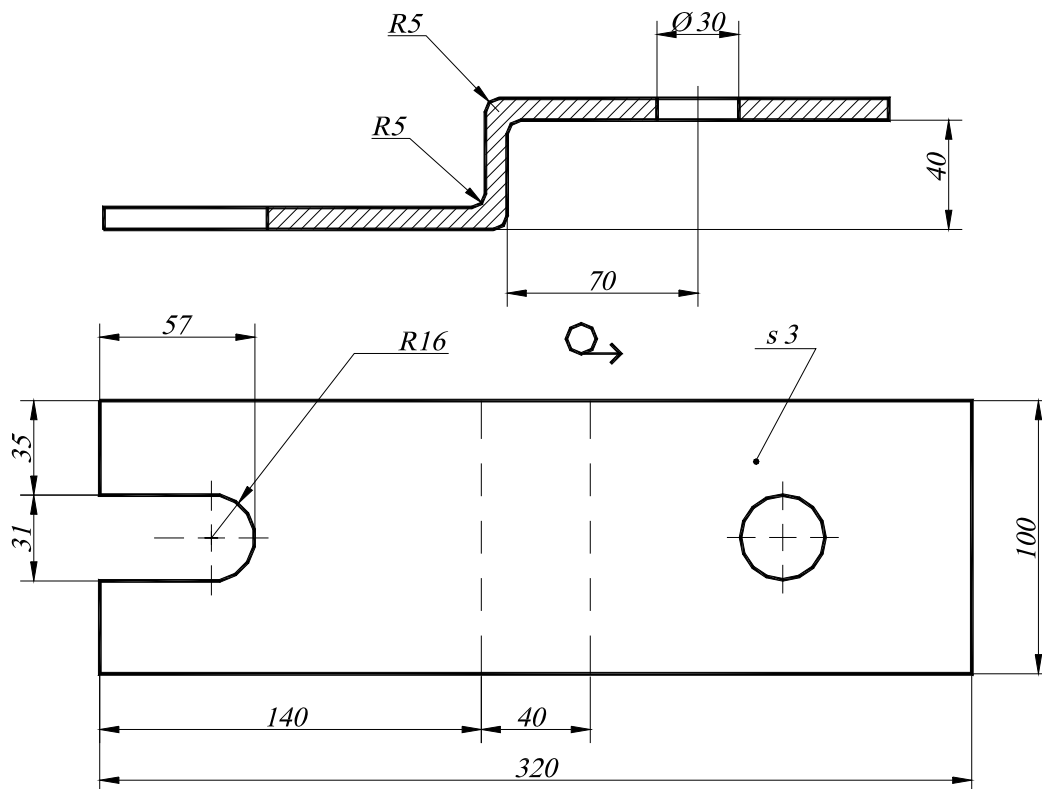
Чертеж детали, изготовленной холодной штамповкой
